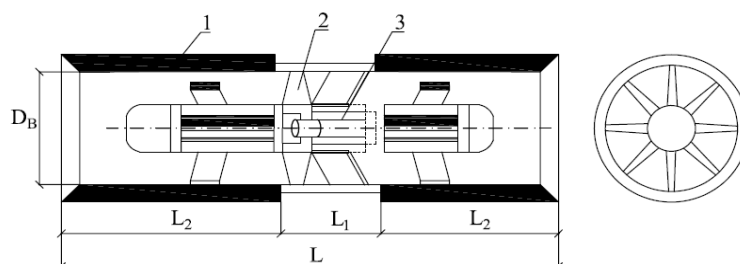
Конструкция реверсивного осевого струйного вентилятора: 1 – корпус вентилятора; 2 – лопасти вентилятора; 3 – электродвигатель
